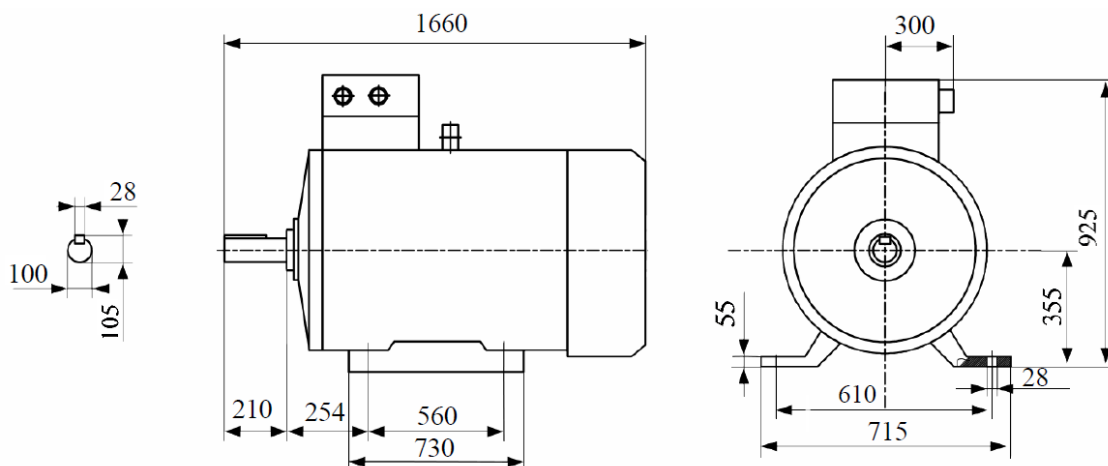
Габаритный чертеж электродвигателя типа А355МLА8
